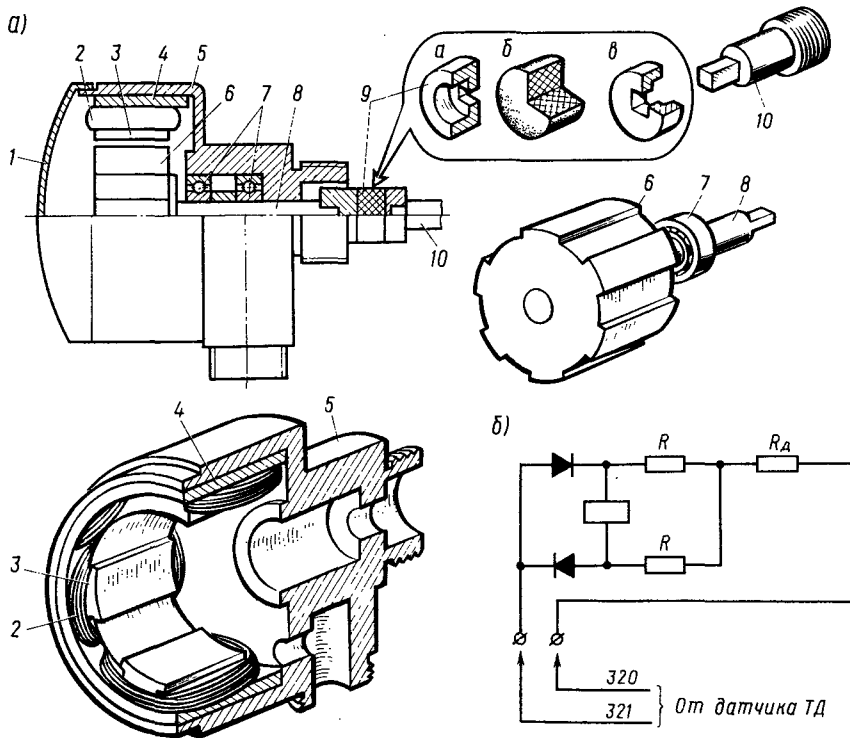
Датчик ТД (а) и схема внутренних соединений приемника ТУ тахометра (б): 1 — крышка; 2 — катушка; 3 — полюсный наконечник; 4 — статор; 5 — корпус; 6 — постоянный магнит; 7 — шариковый подшипник; 8 — вал ротора; 9 — соединительная муфта; 10 — входной вал регулятора дизеля; а, в — втулки; б — слой резины
